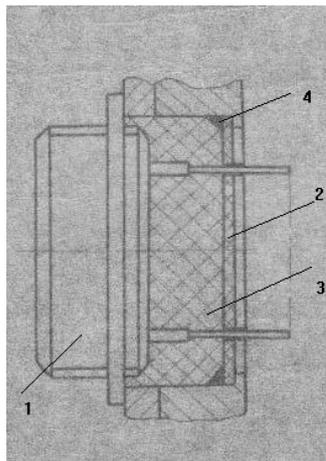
Герметизация корпуса в месте расположения разъема: 1 - герметизированный разъем РПС; 2 - печатная плата; 3 - компаунд; 4 - паяный вакуум-плотный шов
